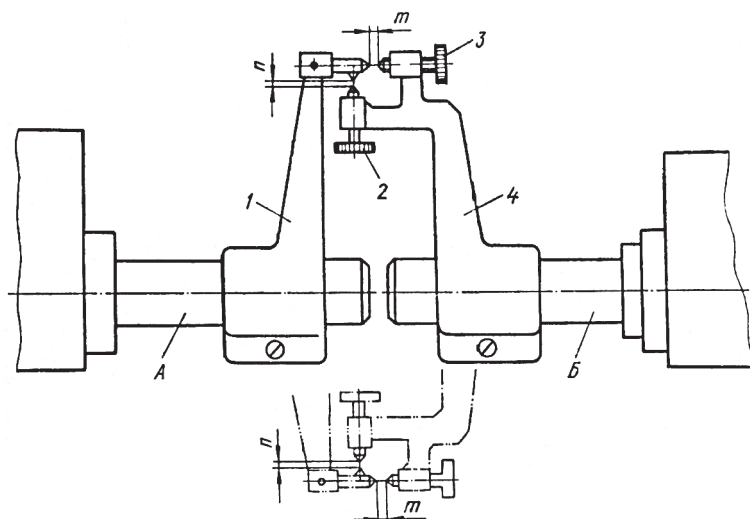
Схема проверки соосности валов с помощью поворотного приспособления
